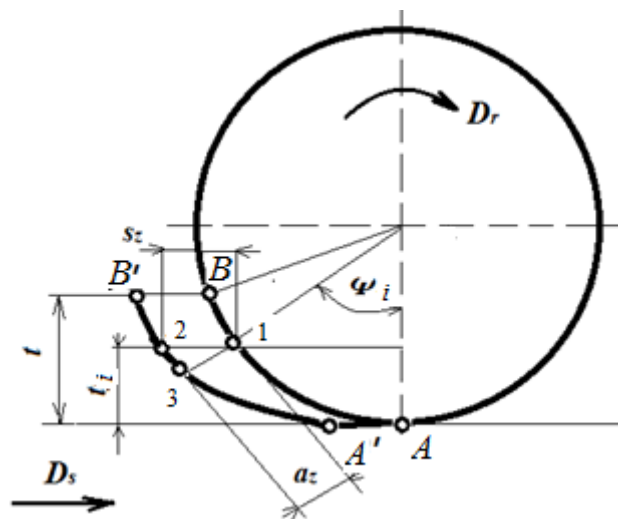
Схема формування товщини зрізу при різанні зубом фрези
